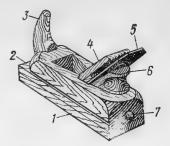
1 — подошва; 2 — корпус; 3 — рог; 4 — клин; 5 — нож; 6 — упор; 7 — пробка
